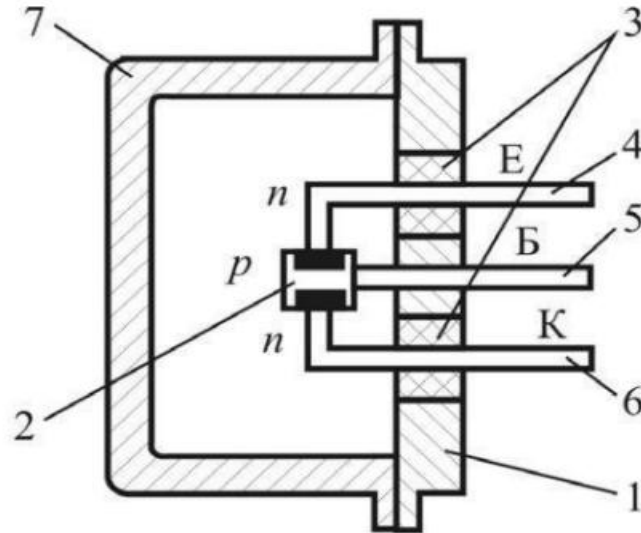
Конструкція малопотужного біполярного транзистора: 1 – основа; 2 – кристал напівпровідника; 3 – ізолюючі втулки; 4, 5, 6 – виводи емітера Е, бази Б, колектора К; 7 – корпус
